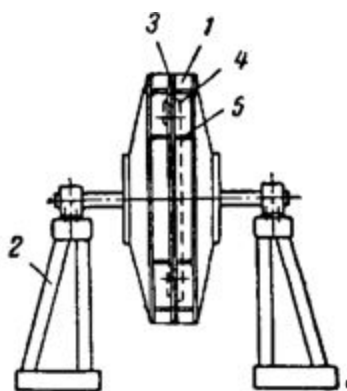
Стенд для одновременной сборки двух крыльчаток
